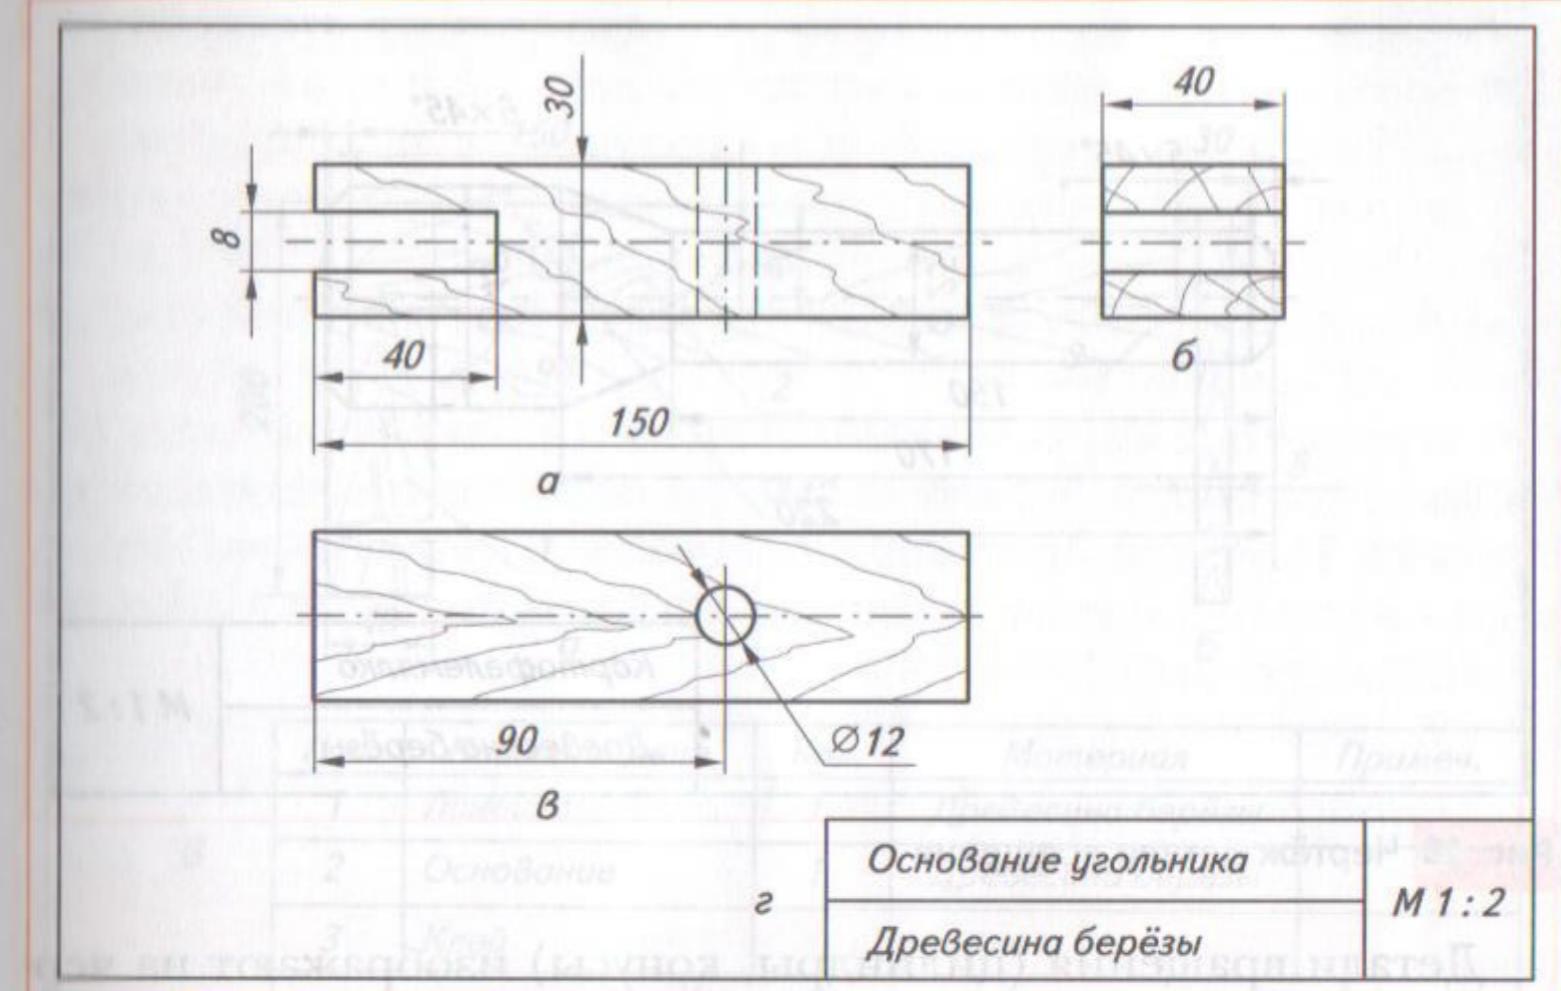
Чертёж основания (колодки) угольника: *а* — главный вид; *б* — вид слева; *в* — вид сверху; *г* — основная надпись
